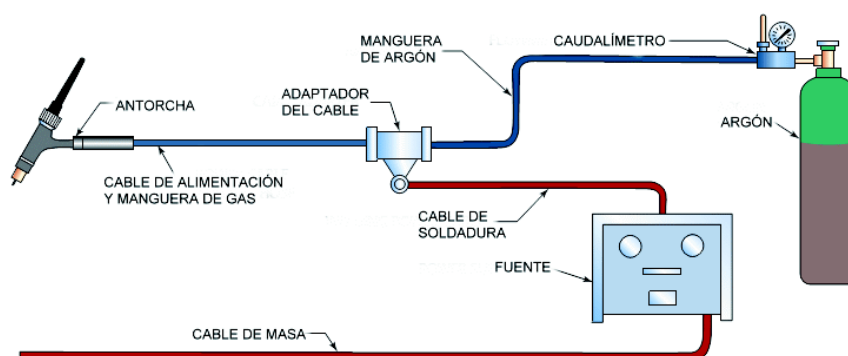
Esquema del circuito de soldadura GTAW con pistola refrigerada por aire⁴³
